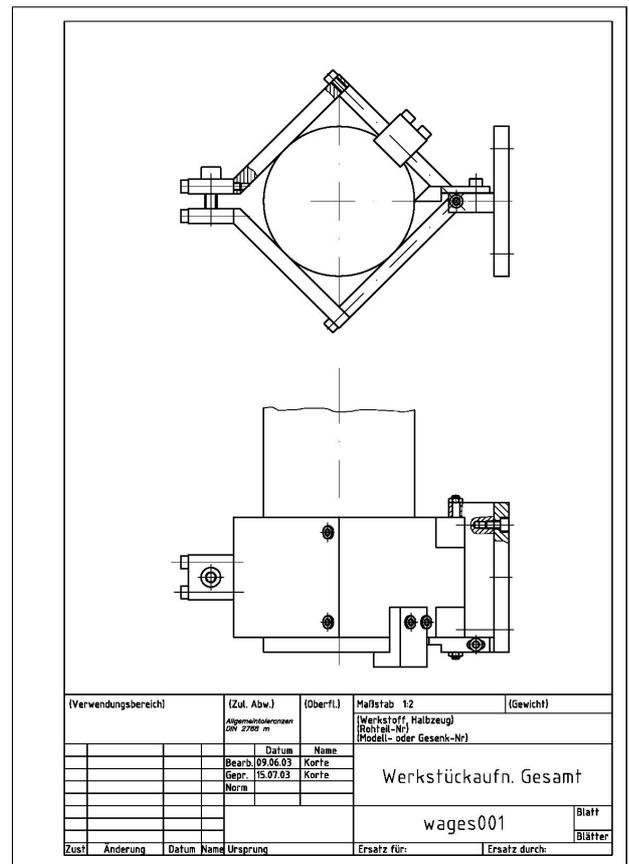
Werkstückaufnahme zur Bearbeitung der Stirnseiten
